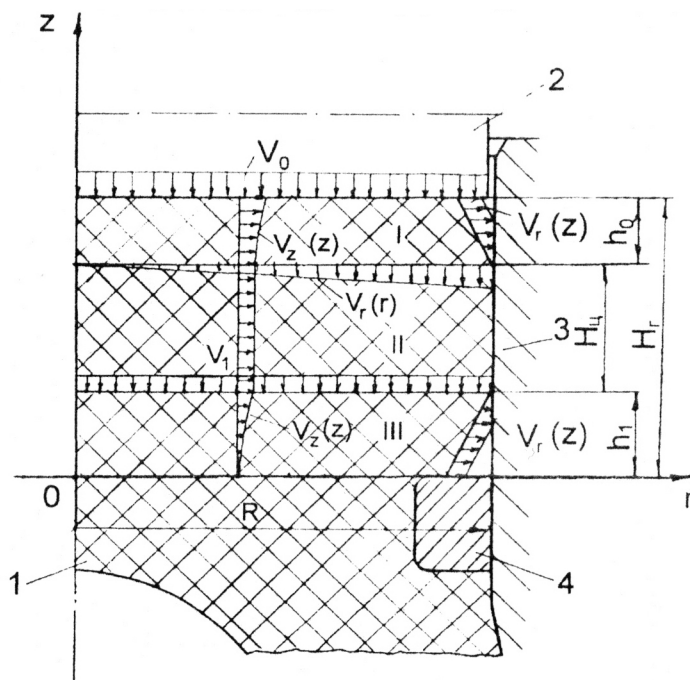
Схема процесса и поля скоростей перемещений частиц металла при заштамповке кольцедержателя биметаллического поршня:
